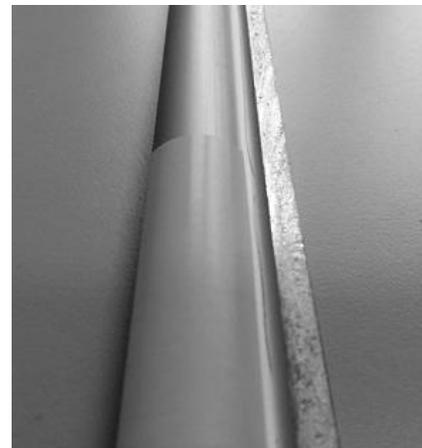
Rollenführung halbrund mit Gleitpapier
